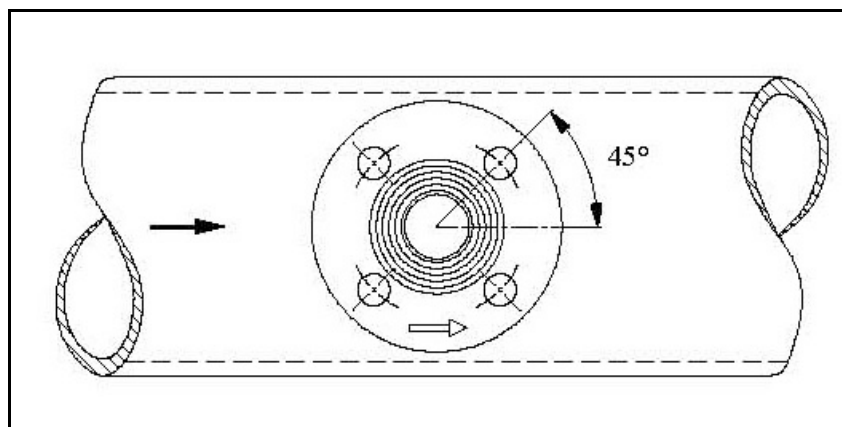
Montage eines Montagestutzens mit Flansch mit 4 Schraubenlöchern
